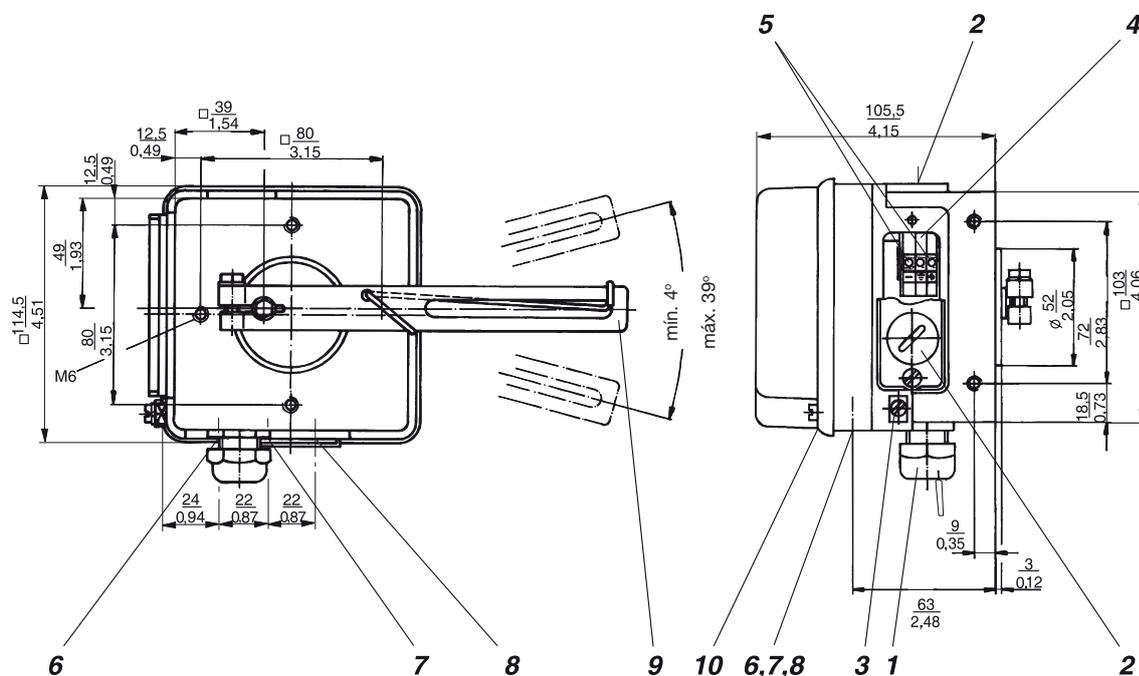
Posicionador com conjunto do transmissor elétrico de posição
